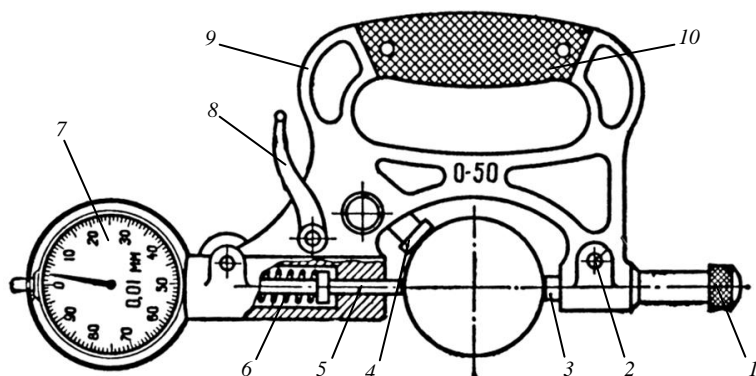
Индикаторная скоба: 1 – предохранительный колпак; 2 – стопор; 3 – переставная измерительная пятка; 4 – регулирующий упор; 5 – подвижная измерительная пятка; 6 – пружина; 7 – индикатор часового типа; 8 – отводной рычаг подвижной пятки; 9 – корпус; 10 – теплоизоляционная накладка
